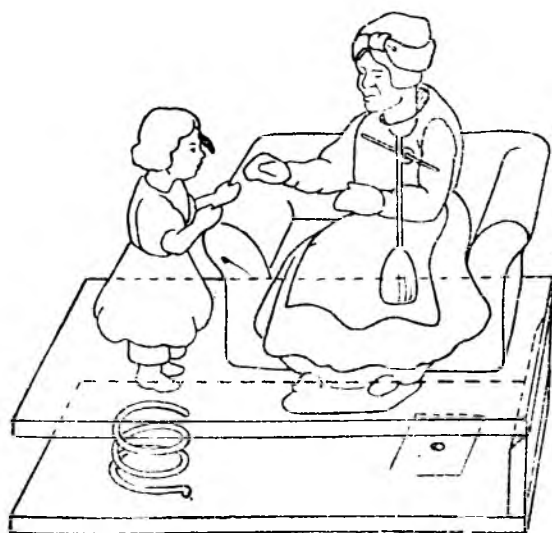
а. Конструкция механизма движения и конструкция пищика (к рис. 43)
